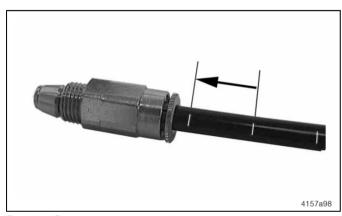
Возвратный клапан с рифленым цанговым патроном для пластмассовой высоконапорной трубы
